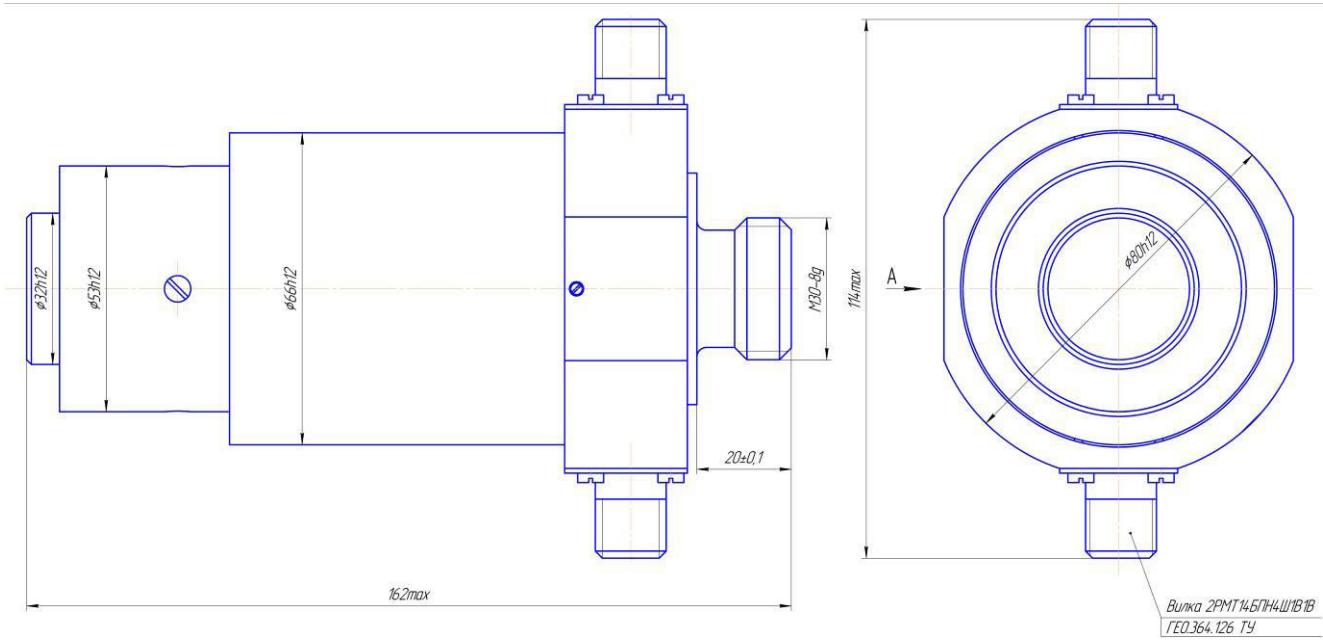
Габаритно-установочные размеры датчика НТ 050
